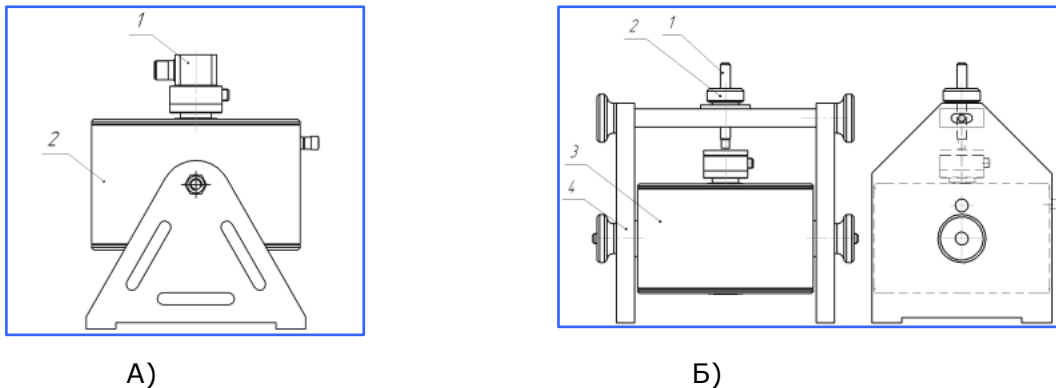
Установка преобразователей вихре токовых Р и вибропреобразователей VPE на виброкалибровочной установке. А) 1 – вибропреобразователь, 2 – виброкалибровочная установка; Б) 1 – преобразователь вихре токовый; 2 – цапговый зажим; 3 – виброкалибровочная установка; 4 – опоры виброкалибровочной установки
